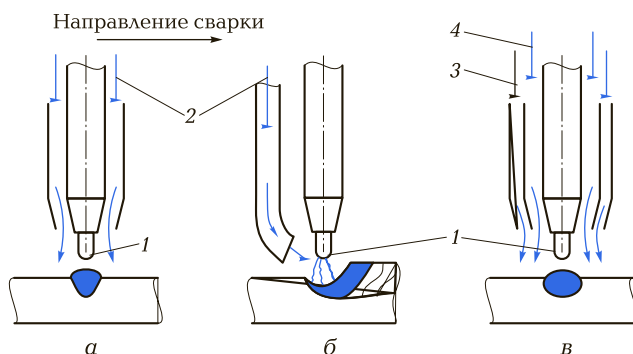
Схемы газовых потоков в зоне сварки:
